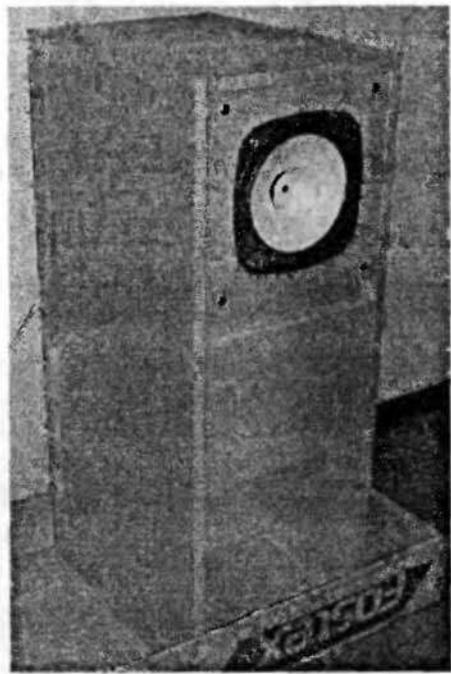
Корпус собран. На боковой стенке видны головки шурупов
